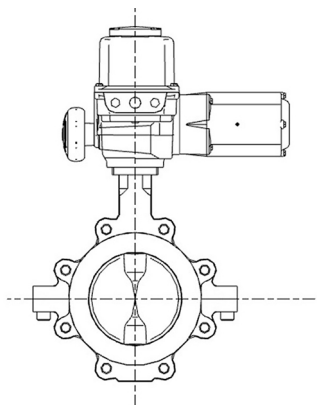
Schnittzeichnungen KE Elastomer für DN 40 - 300
